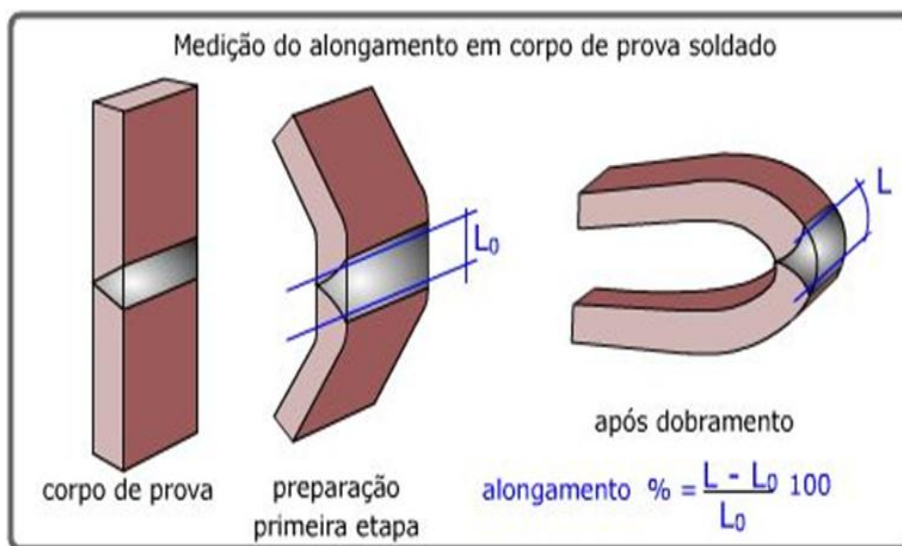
Medição do alongamento de um corpo de prova soldado.
